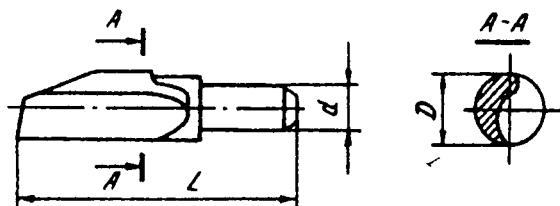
Фрезы концевые цилиндрические однозубые
